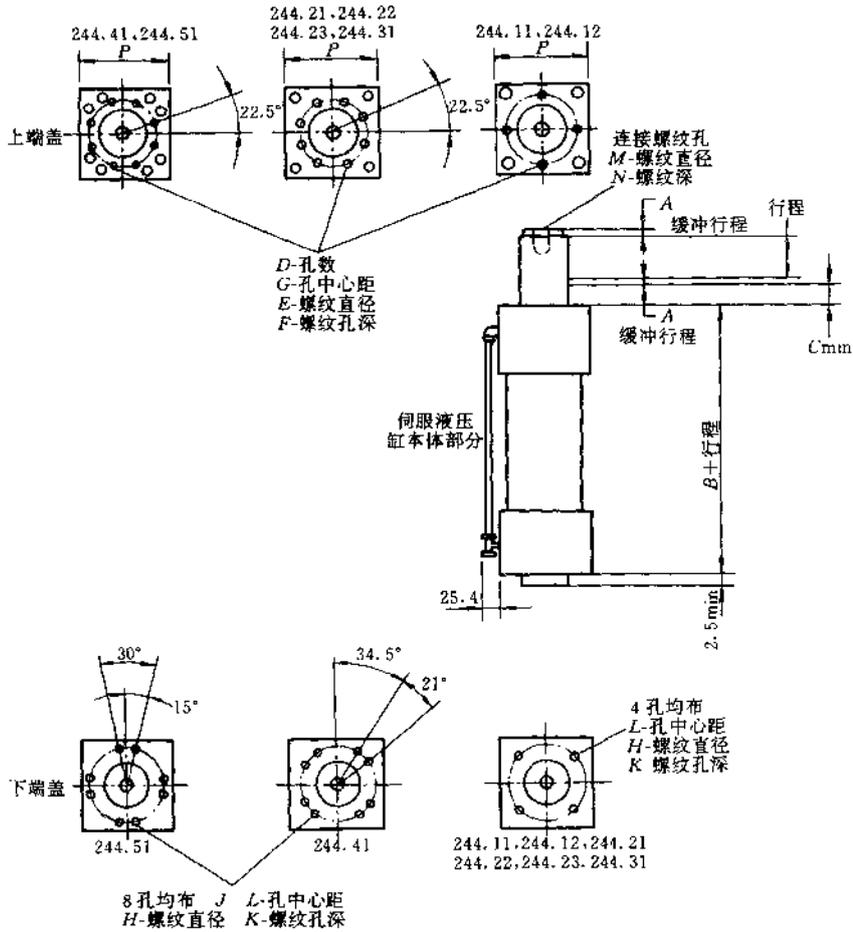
MTS244 系列基本型伺服液压缸外形尺寸图
